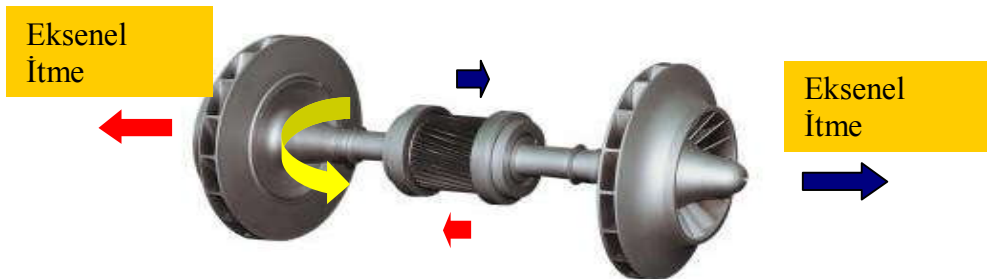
Kompresör bıçaklarının montaj şekli
